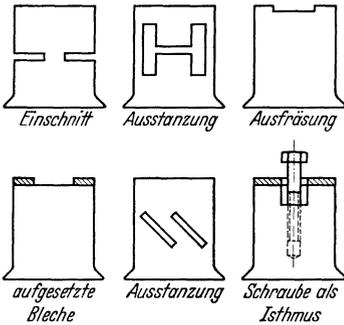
Polformen mit Isthmus für die Erregermaschine eines Synchronstromerzeugers.
